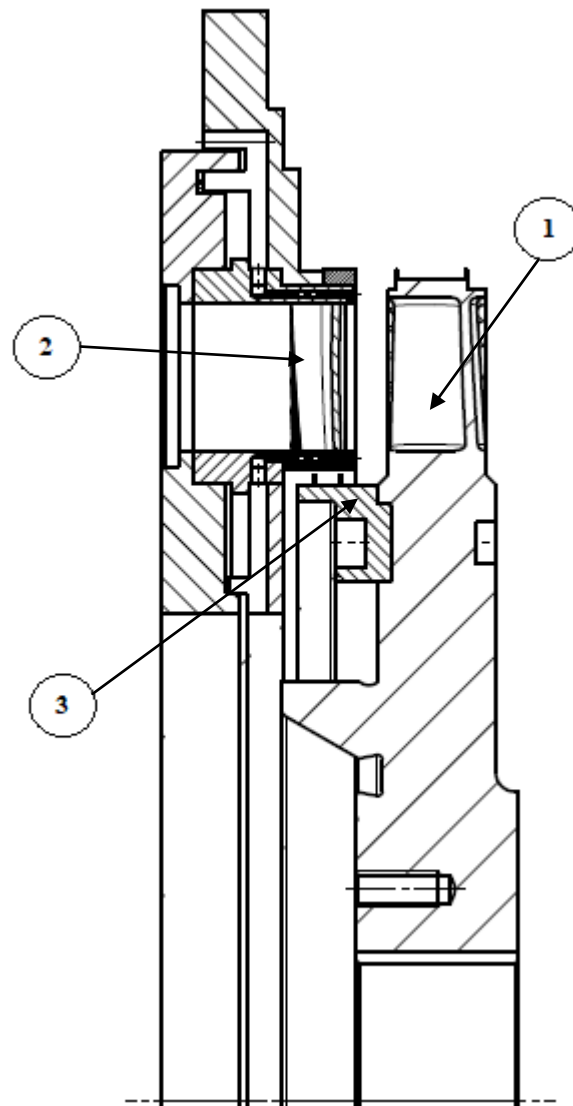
Experimentální zařízení v laboratořích KKE [10]
